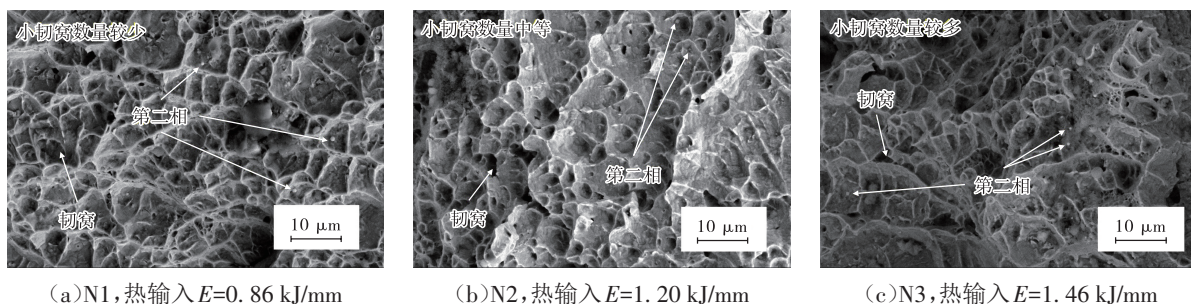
316LN奥氏体不锈钢焊接接头断口形貌
